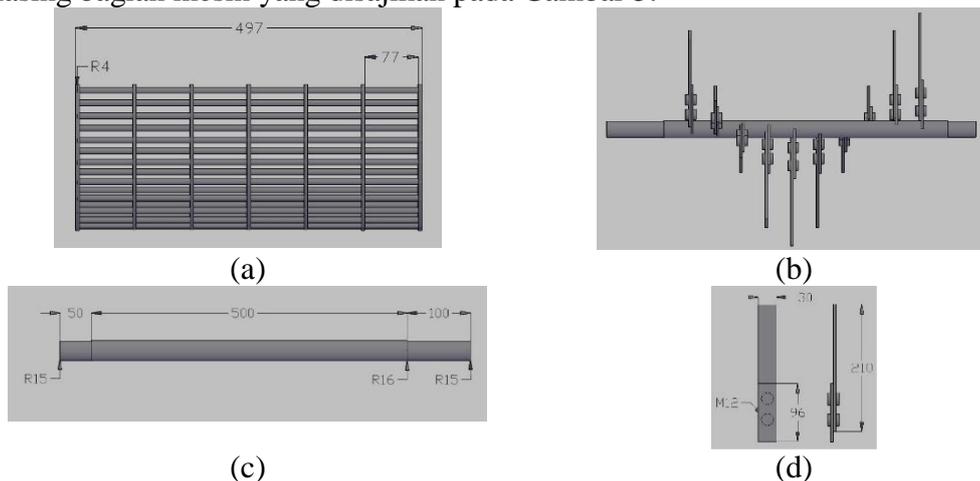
Tampak Tiga Dimensi Mesin Pengurai Sabut Kelapa
